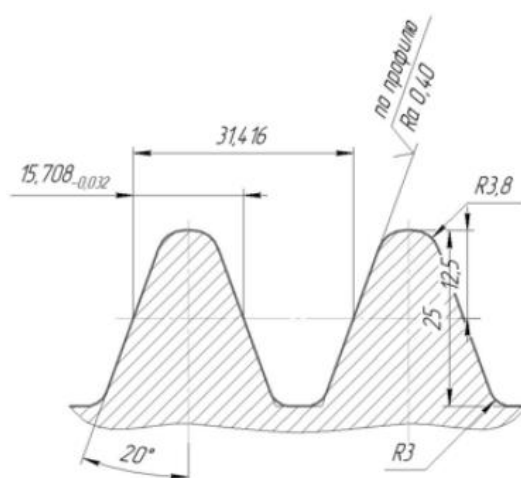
Профіль зубів черв'ячної фрези
